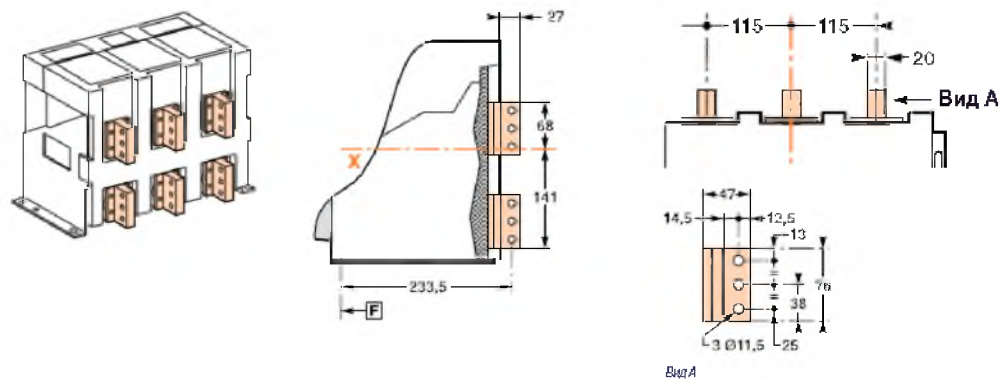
Горизонтальные и вертикальные выводы для заднего присоединения с присоединительными размерами для ВА–СЭЩ–АС40 стационарного исполнения
